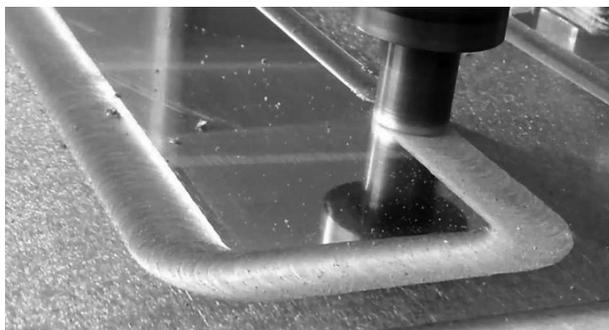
Общий вид сварного соединения выполненного СТП
